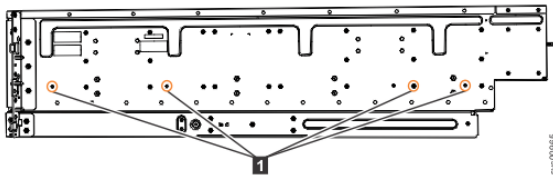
Positionen der Schrauben zum Anbringen der inneren Schiene am Gehäuse
